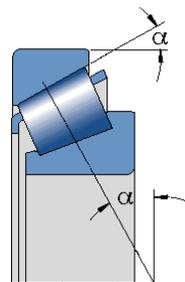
Ángulo de contacto de un rodamiento cónico
